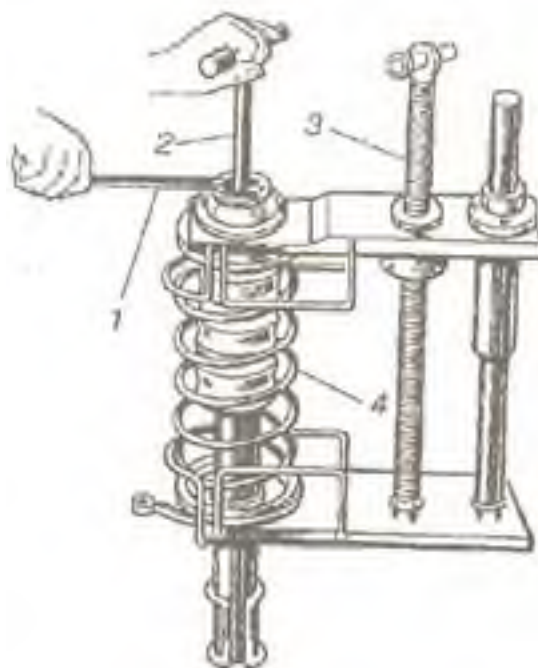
Разборка телескопической стойки автомобиля АЗЛК-2141 в приспособлении для разборки-сборки:
